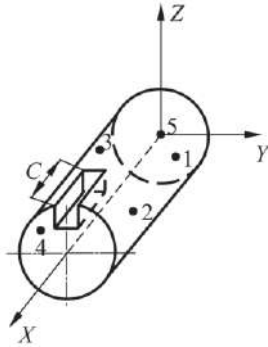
Установка заготовки з позбавленням п'яти ступенів свободи
